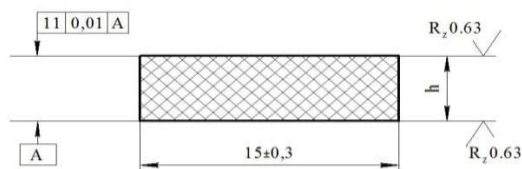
Креслення зразка / Fig. 3 Drawing a sample
